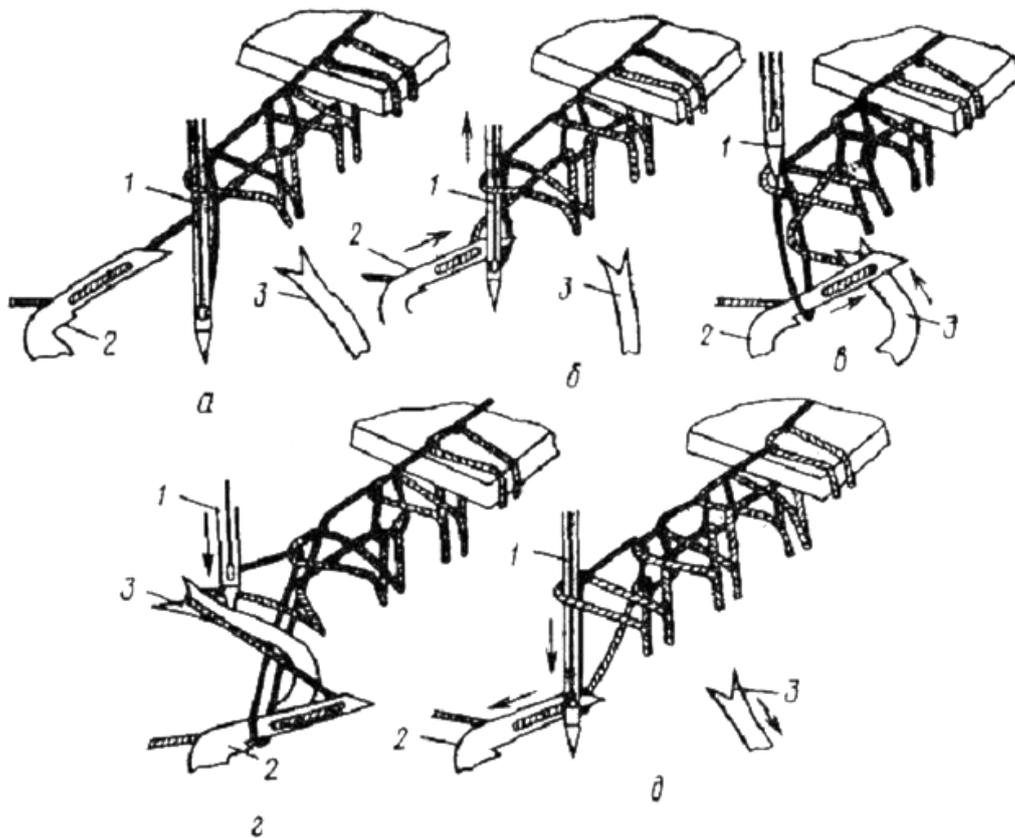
Образование двухниточного цепного обметочного переплетения
